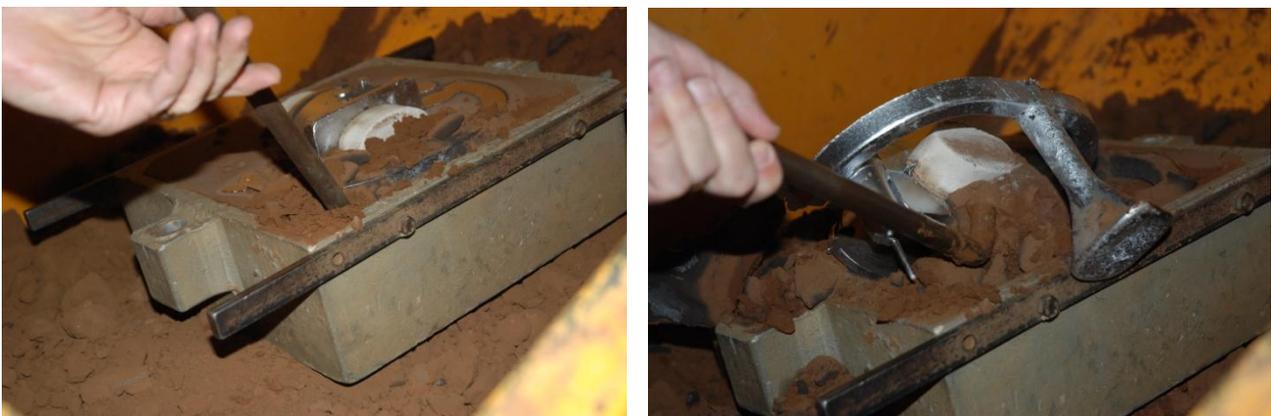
Destruction du moule pour extraire la pièce brut de moulage et son noyau inclus
